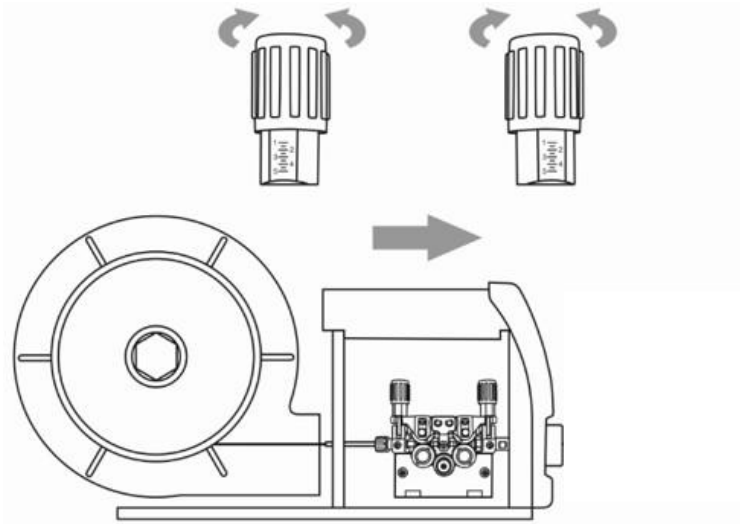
Усилие зажатия сварочной проволоки.
